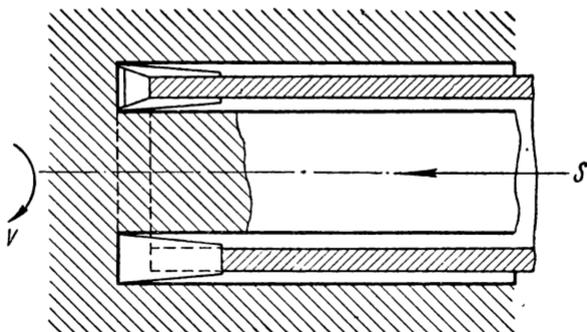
Сверление глубоких отверстий с вырезанием кольцевой канавки
